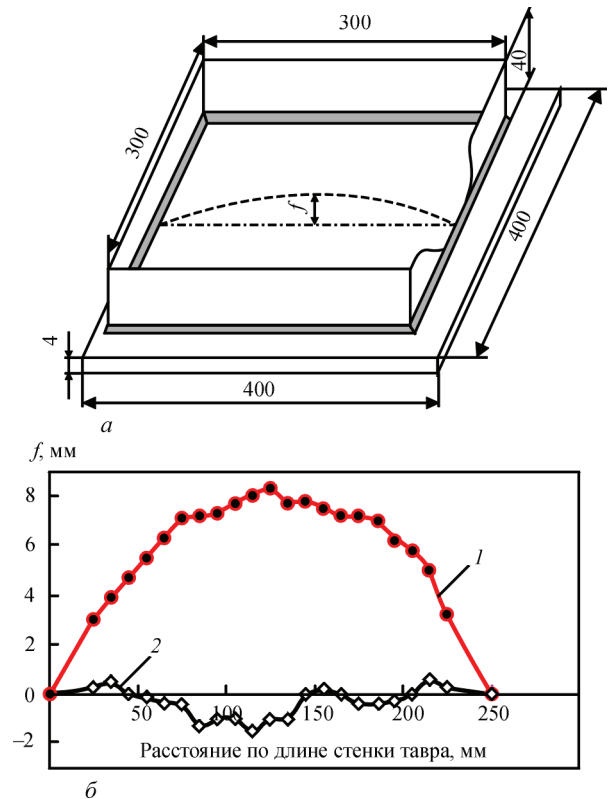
Образец сварного соединения из сплава АМг6 с бухтиной: а — схема образца (f — прогиб); б — формоизменения образца (кривая 1 — исходные прогибы f по центру образца; 2 — f после ЭДО)
